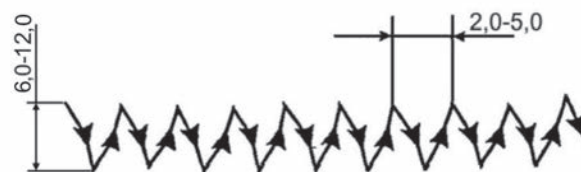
Схема перемещения электрода с поперечными колебаниями при сварке в защитных газах
